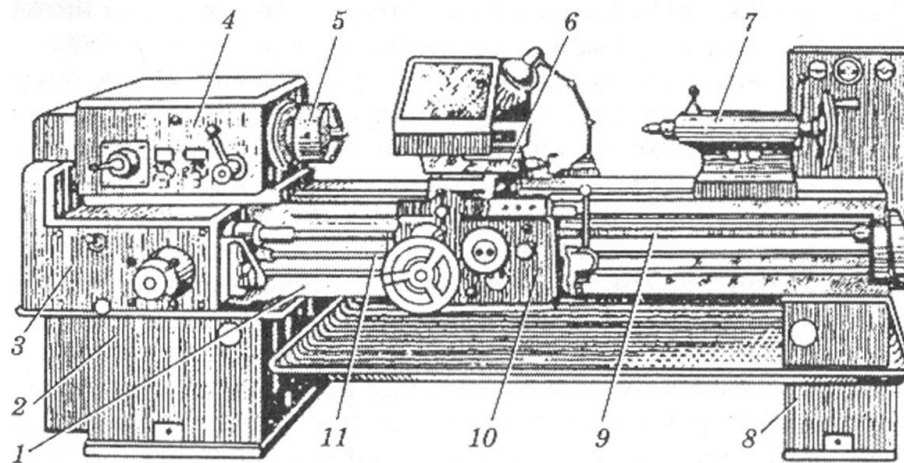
Токарно-гвинторізний верстат 1К62
